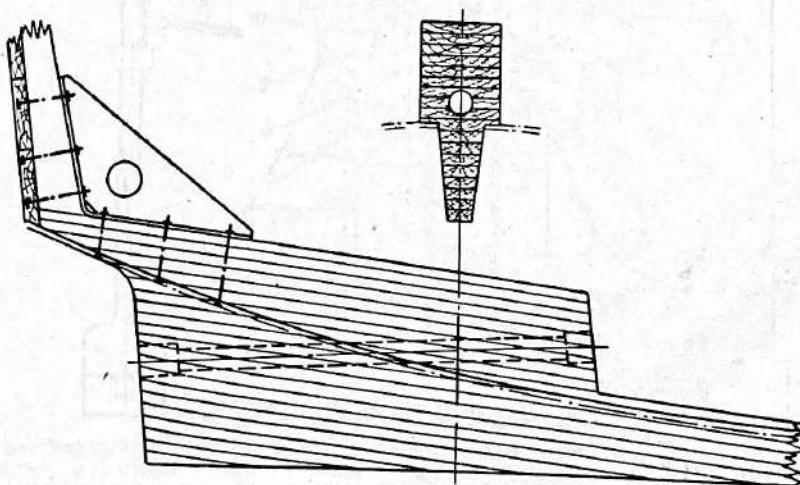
Набор кормового дейдвуда для катера (клеенный вариант).
